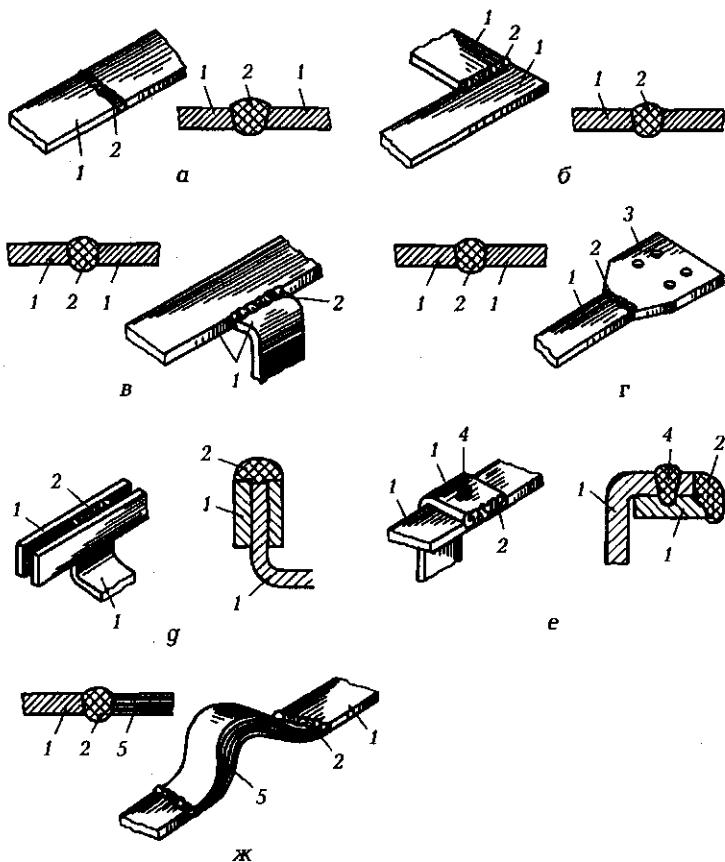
Варианты сварных соединений и ответвлений для прямоугольных шин:
